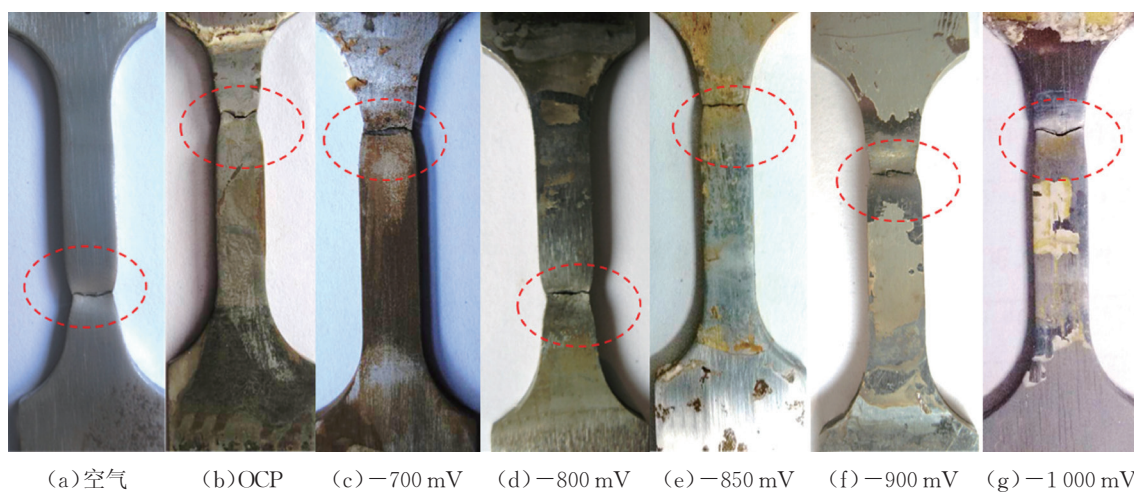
X80 焊接接头试样断裂后的宏观形貌
